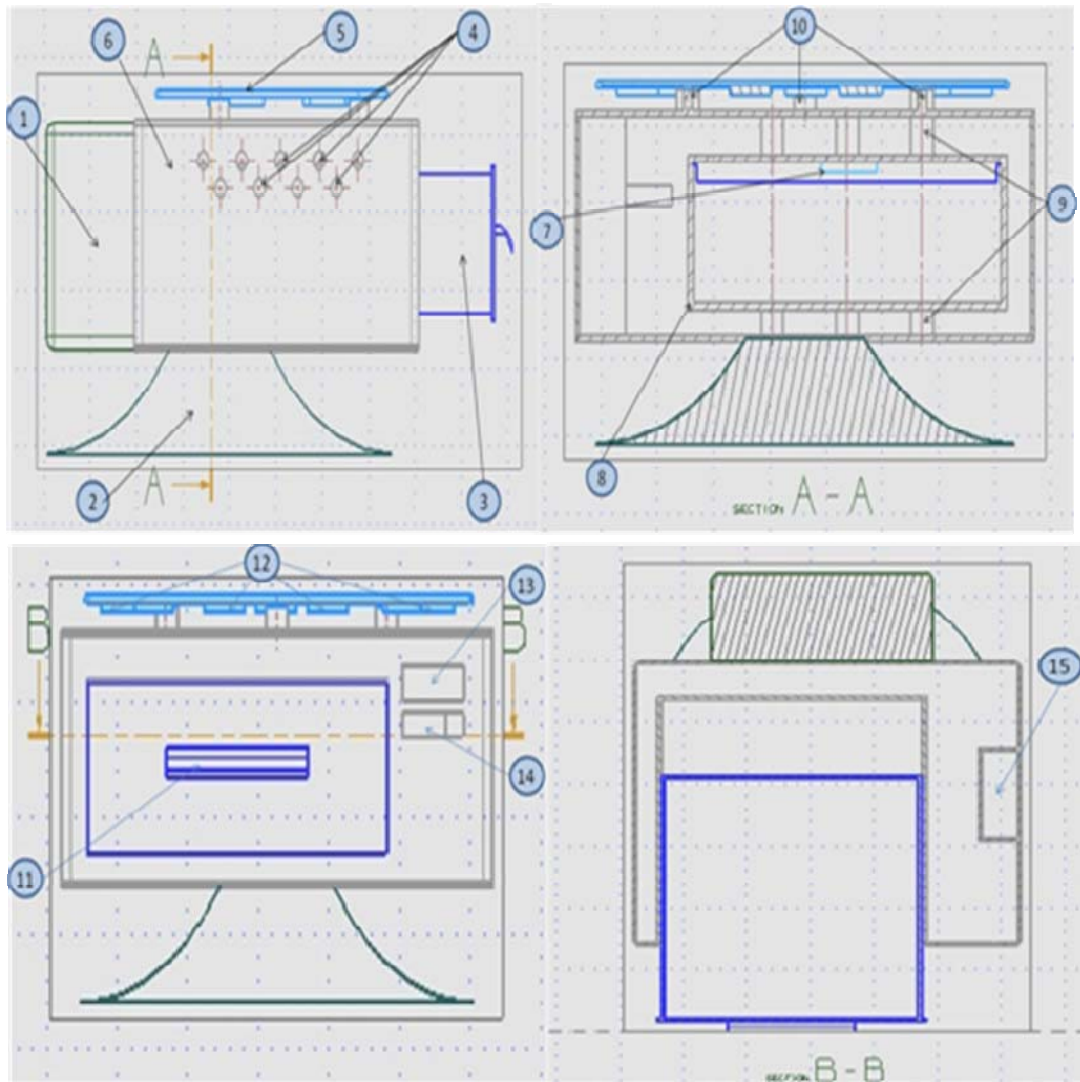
Vistas obtenidas del plano de conjunto del segundo diseño.
